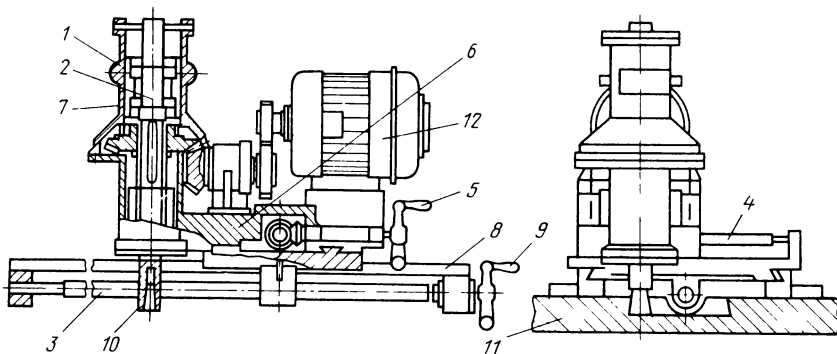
Приспособление для механообработки корпусных деталей без демонтажа
